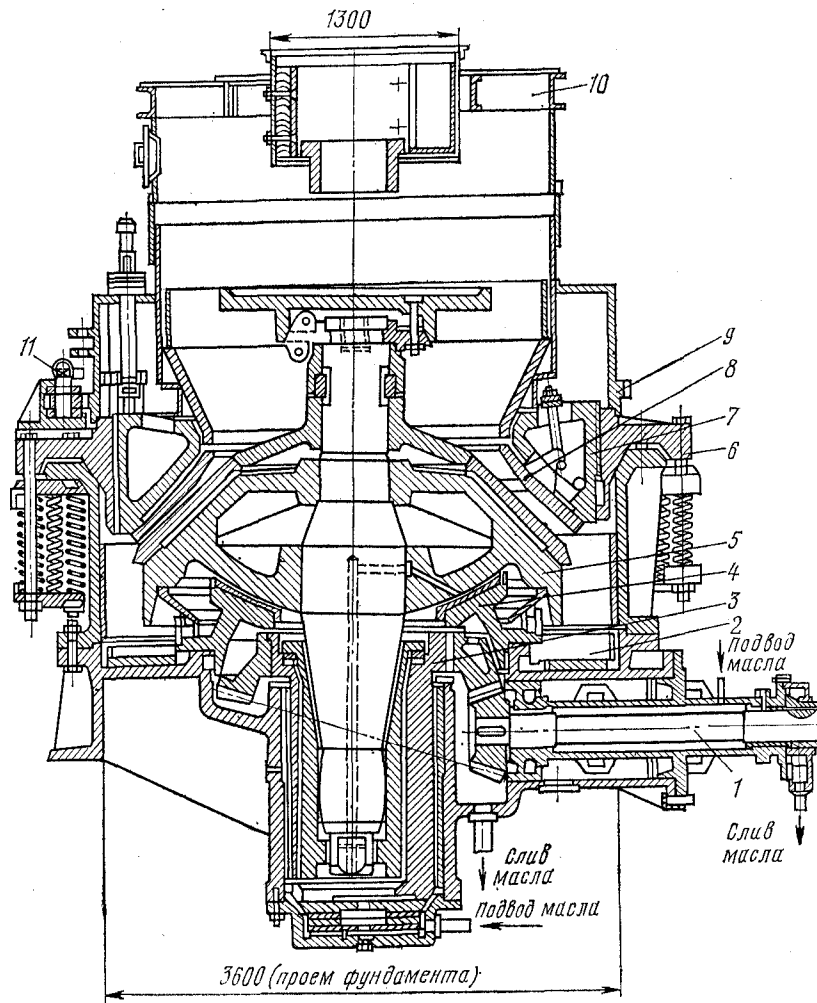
Конусная дробилка для мелкого дробления КМД-3000Т
